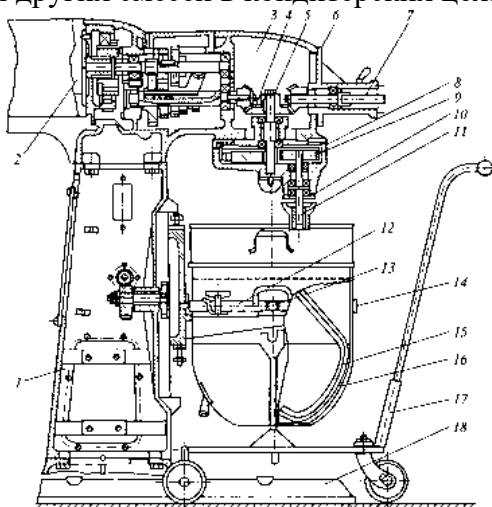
Взбивальная машина МВ-60: 1 - станина; 2 - электродвигатель; 3 - коробка скоростей; 4 - коническое колесо; 5 - вертикальный вал; 6 - корпус вала отбора мощности; 7 - вал отбора мощности; 8 - нижняя крышка; 9 - сателлит; 10 - рабочий валик; 11 - штифт; 12 - подставка; 13 - фиксатор; 14 - кольцо бачка; 15 - сбиватель; 16 - бачок; 17 - тележка; 18 - плита
